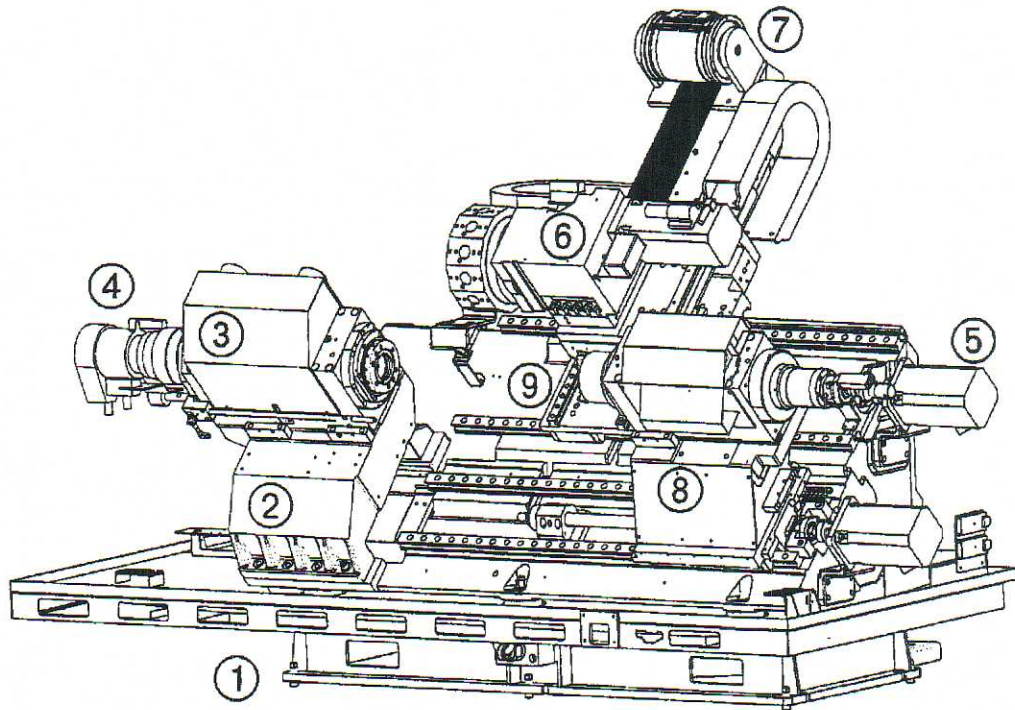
Проставить номера базовых деталей и механизмов станка с ЧПУ
